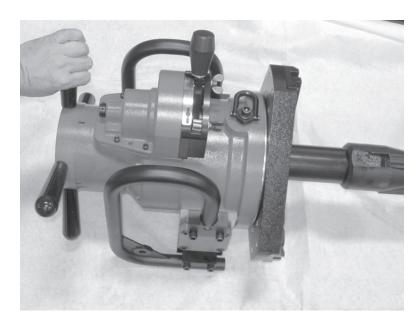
Поворачивайте ручку подачи против часовой стрелки до свертывания резьбы оправки с гайки механизма подачи.
